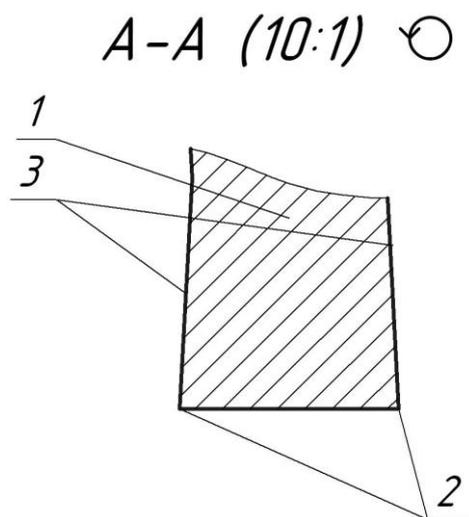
Конструкция инструмента червячного типа (сечение А-А)
